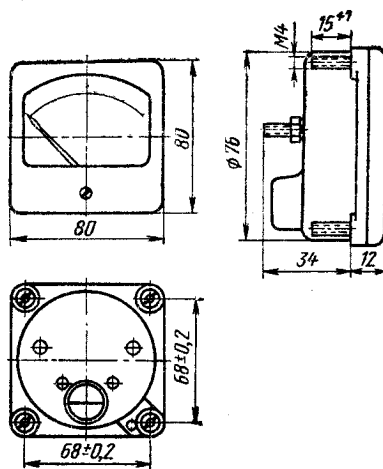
Габаритный чертеж прибора типа М4200.
